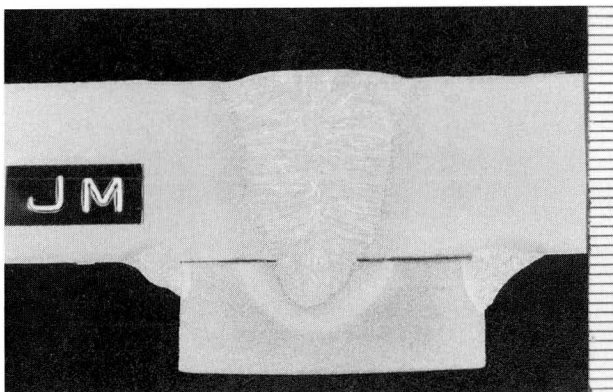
エレクトロガスアーク溶接直継手断面マクロ写真
